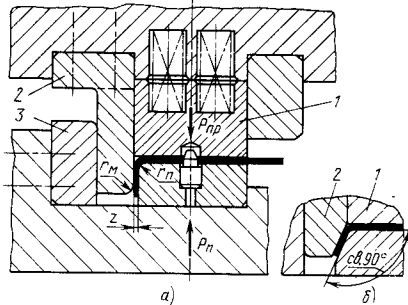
Одноуголовая (L-образная) гибка (полкой вниз) с защемлением исходной заготовки в горизонтальном положении
